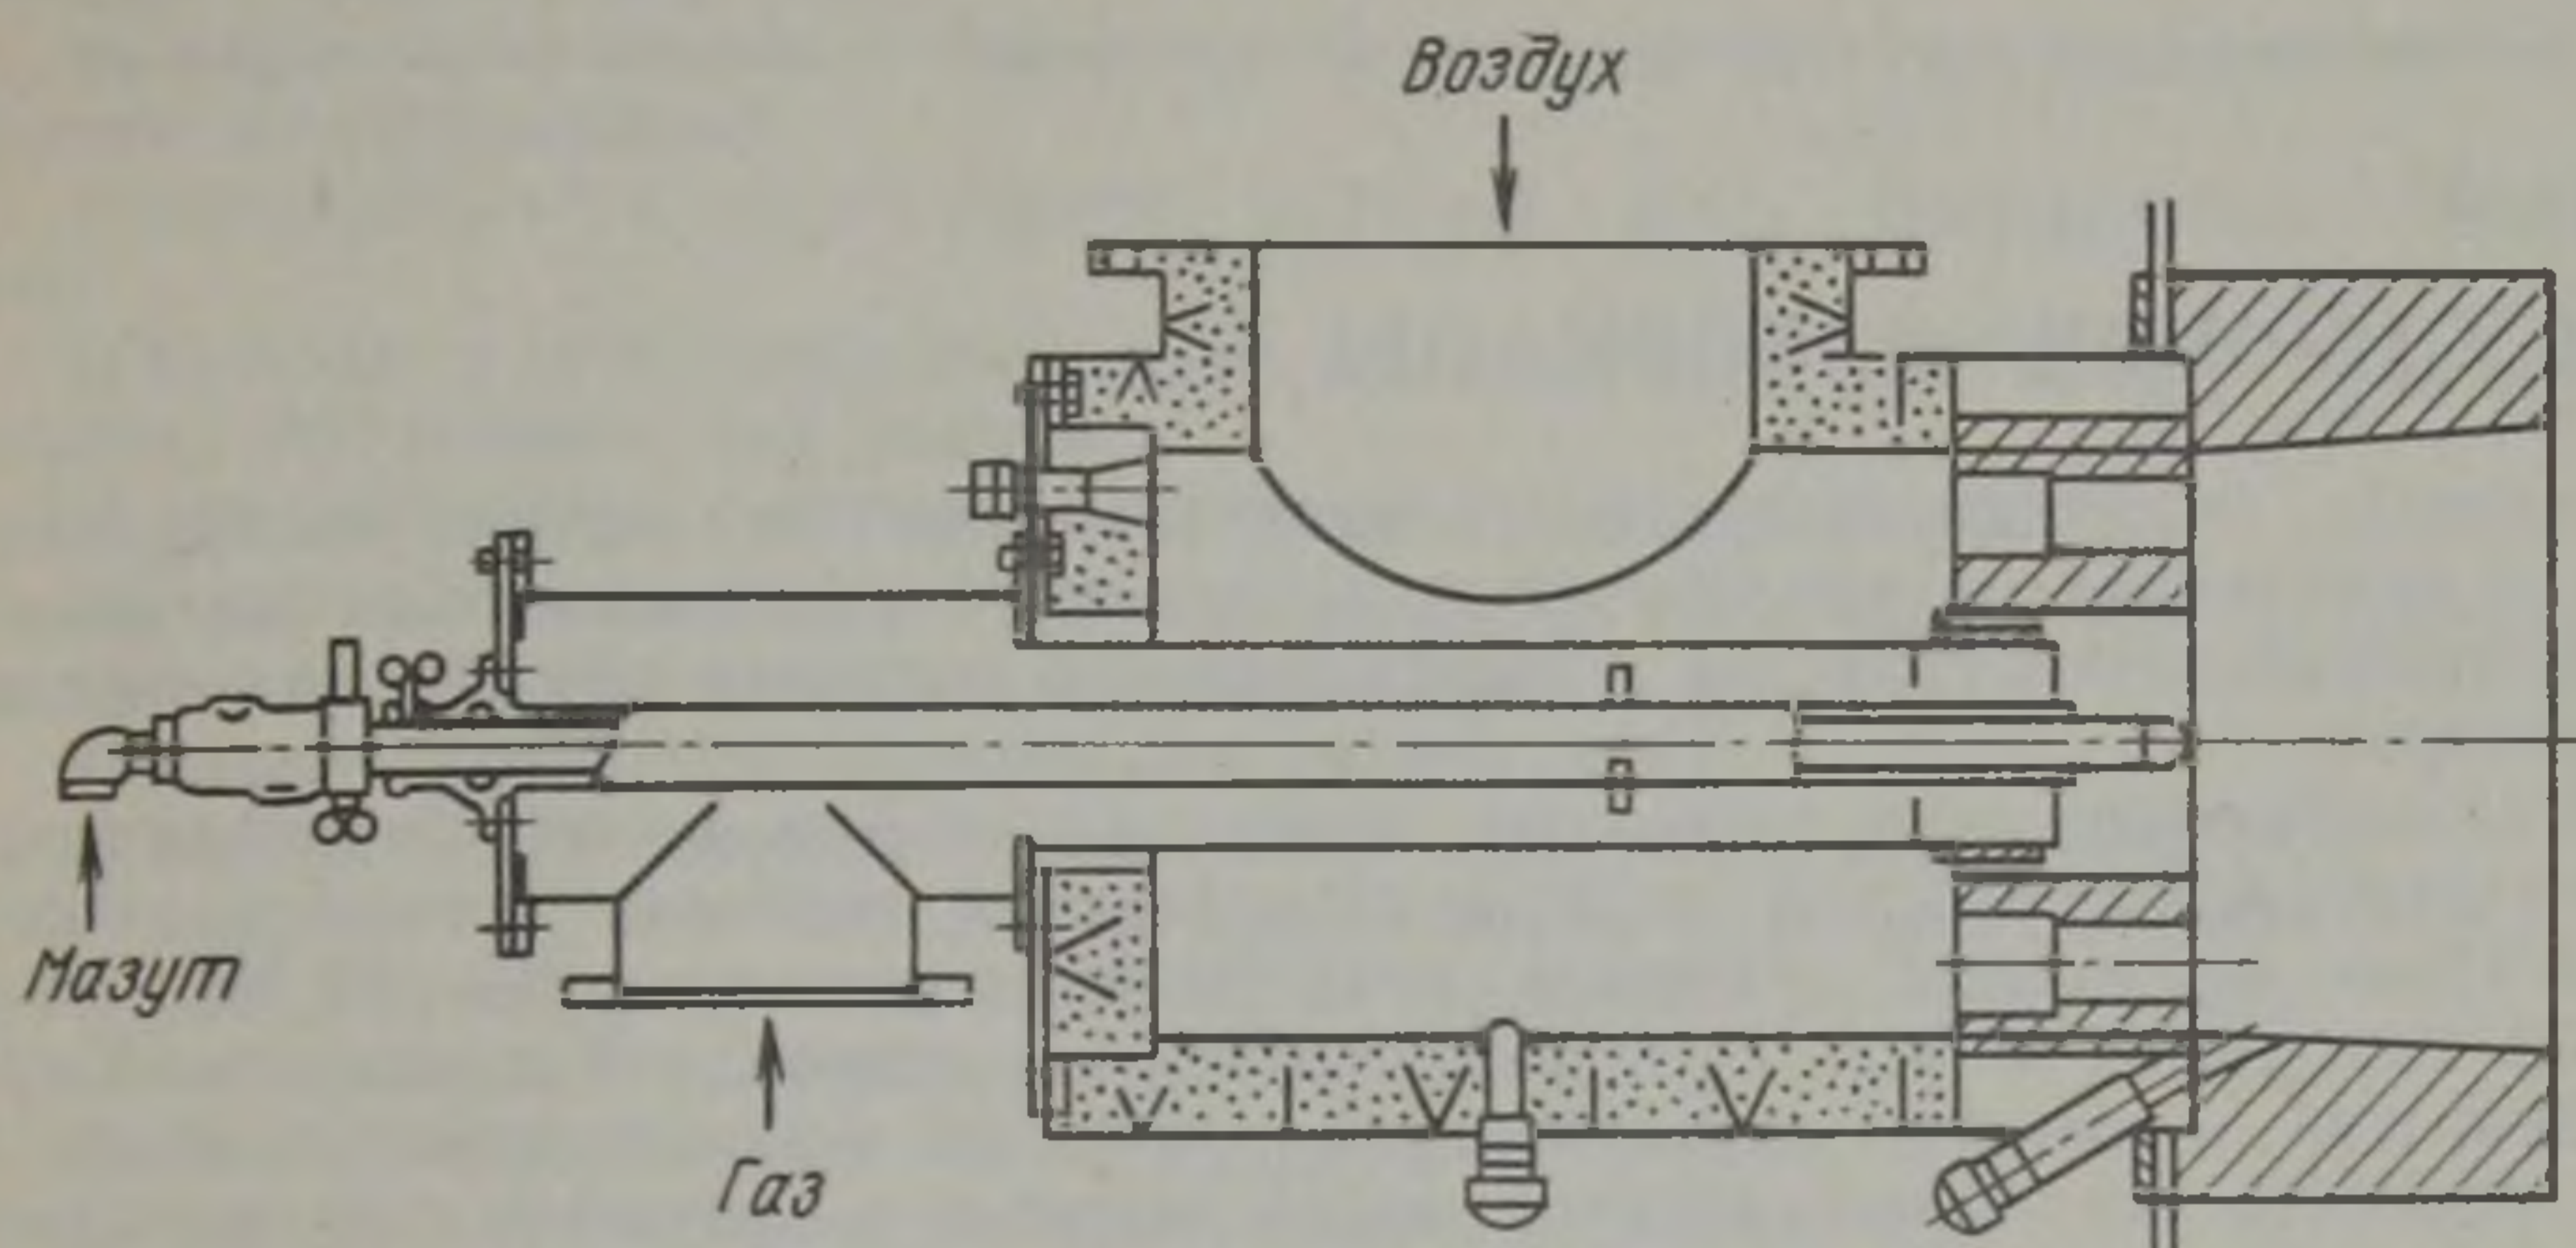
Комбинированная газо-мазутная горелка для нагревательных печей
